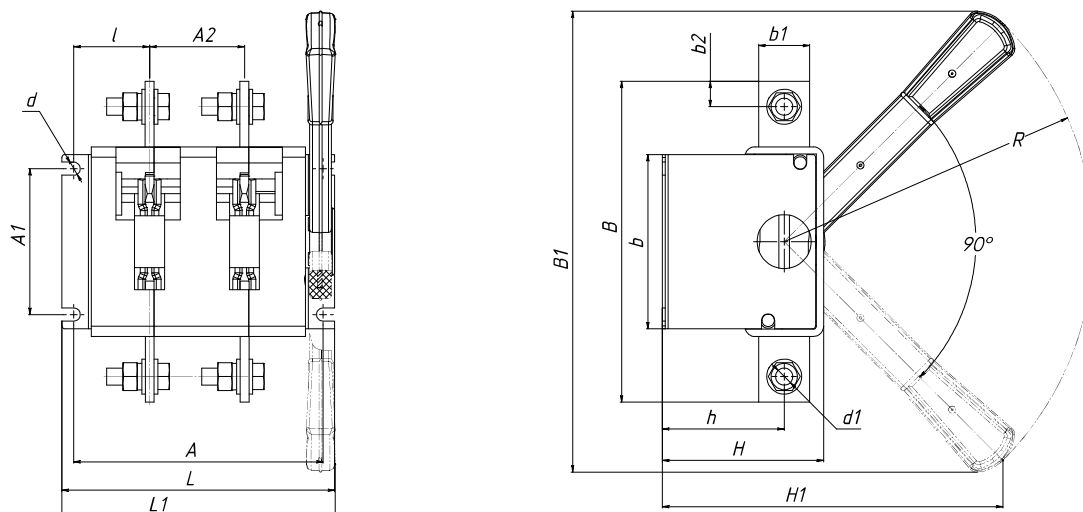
Выключатель-разъединитель на одно направление двухполюсный с боковой ручкой
